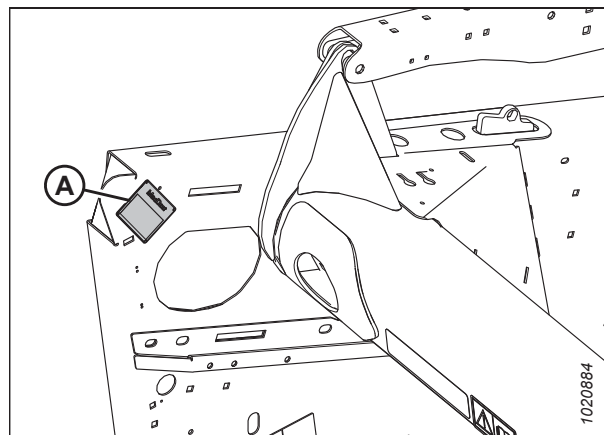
Emplacement de la plaque du numéro de série de la plateforme
